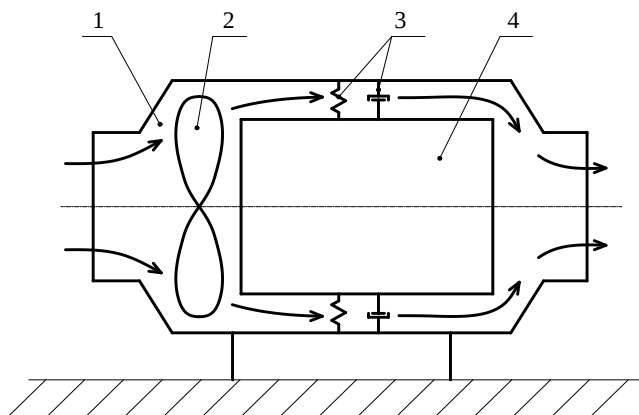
Конструктивная схема вентилятора: 1 – корпус, 2 – крыльчатка, 3 – амортизированный узел крепления вентилятора к корпусу, 4 – электродвигатель
